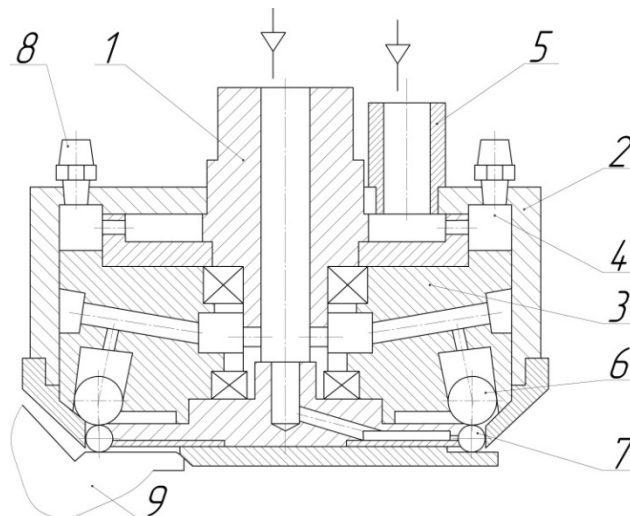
Конструкционная схема инструмента: 1 – полый вал; 2 – корпус; 3 – диск; 4 – лопатки; 5 – штуцер; 6 – приводящие шары; 7 – деформирующие шары; 8 – глушители; 9 – заготовка
